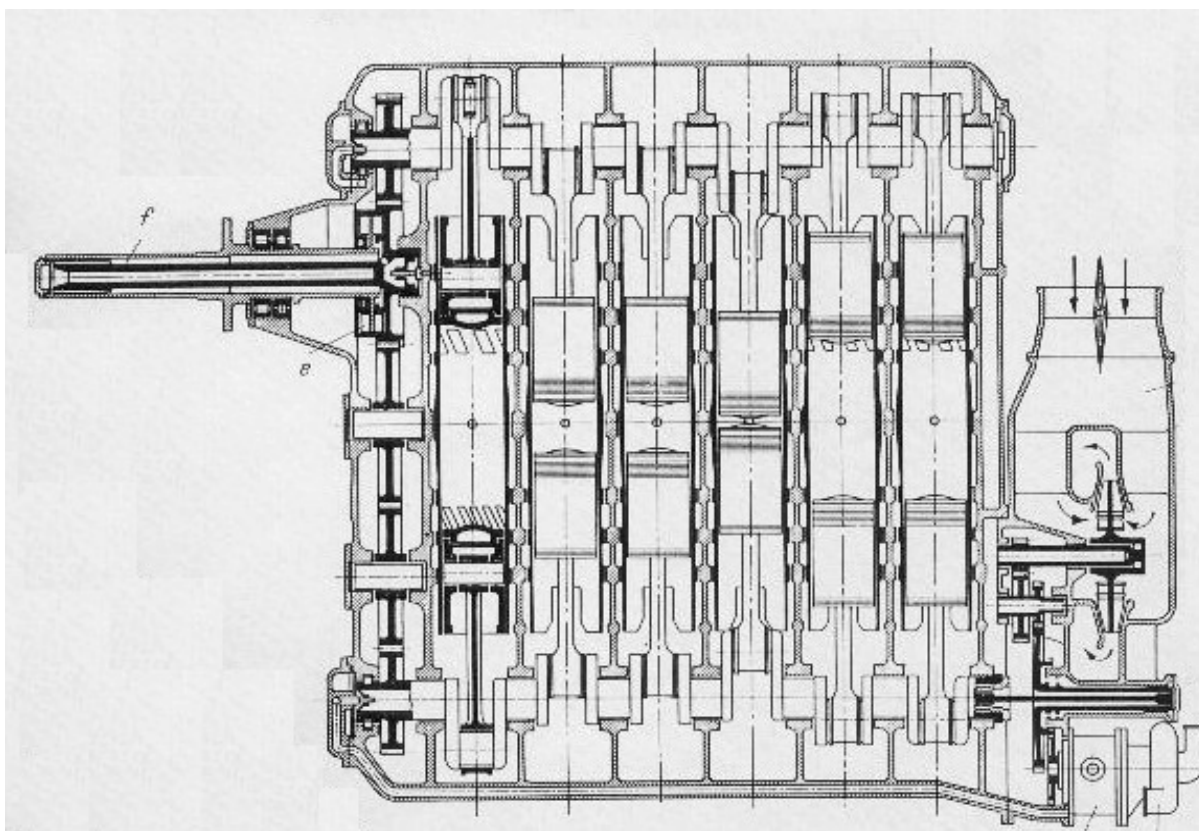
Авиационный двухтактный 6-цилиндровый 12-поршневой двухвальный дизельный двигатель жидкостного охлаждения с вертикальным расположением цилиндров и встречно-движущимися поршнями фирмы «Юнкерс»
